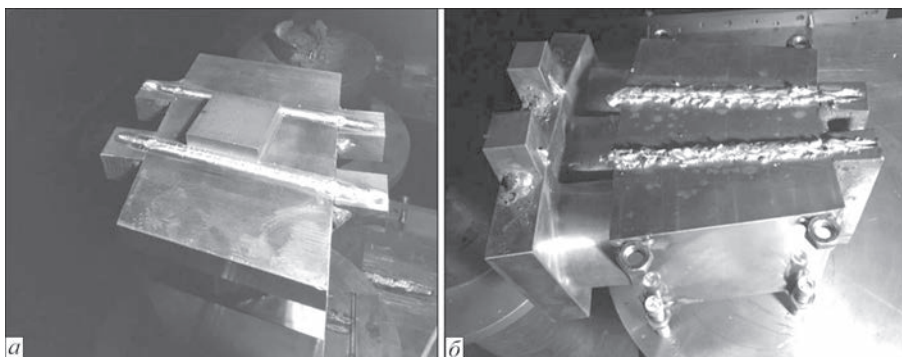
Зовнішній вигляд пакету лопаток з товщиною хвостової частини 120мм, виготовлений за допомогою ЕПЗ: а – вигляд бандажної частини пакету; б – вигляд хвостової частини пакету
